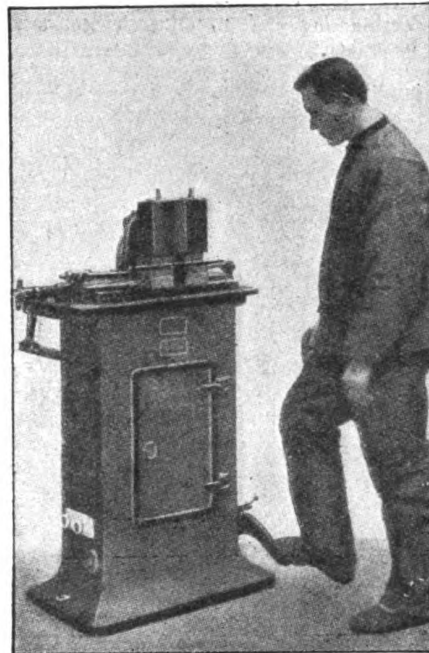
Selbsttätige Stumpfschweißmaschine
